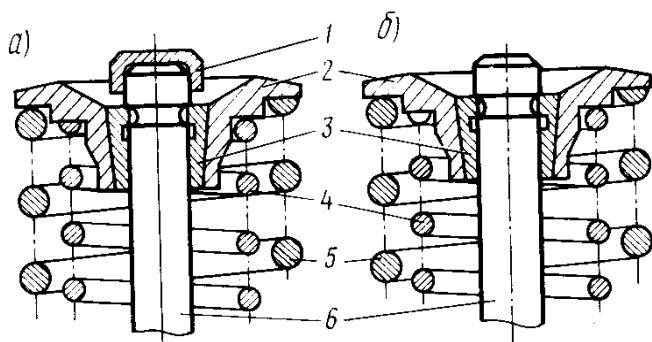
Клапаны: а—выпускной; б—впускной; 1 — наконечник выпускного клапана; 2 — тарелка пружин клапана; 3 — сухарь клапана; 4 — внутренняя пружина клапана; 5 — наружная пружина клапана; 6 — клапан
